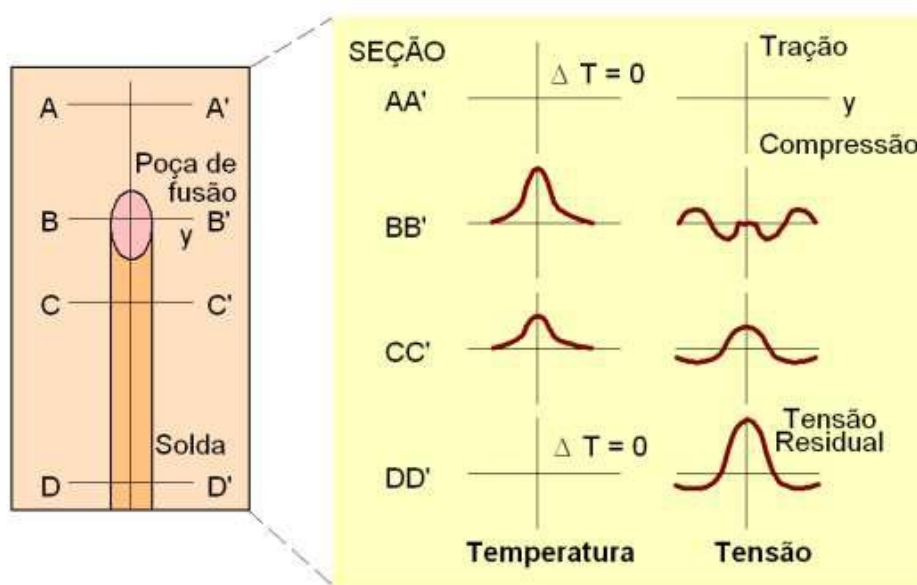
Desenvolvimento de tensões residuais longitudinais durante a soldagem [1]
